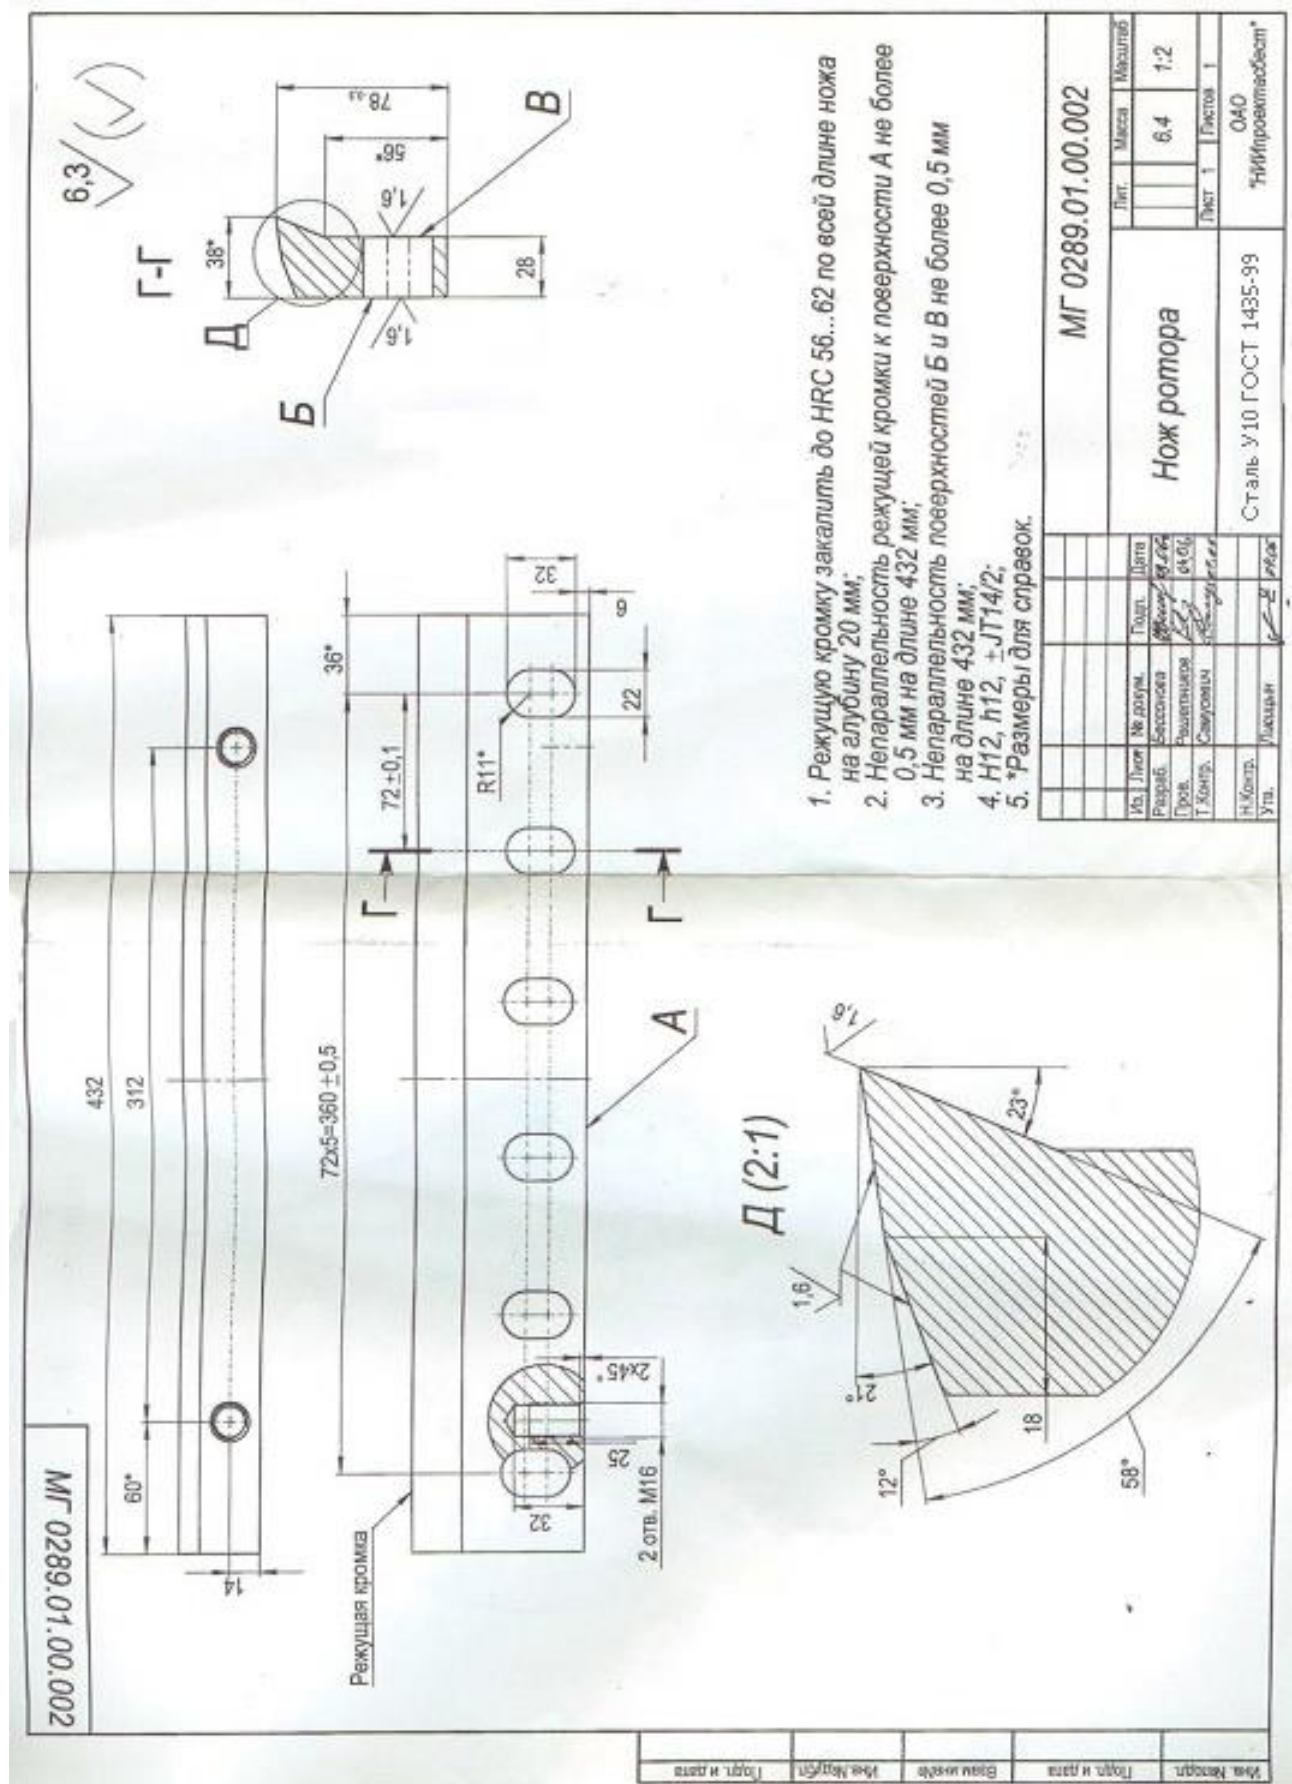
Чертеж ножа для измельчения аккумуляторных полипропиленовых корпусов, изготавливаемого из стали У10
